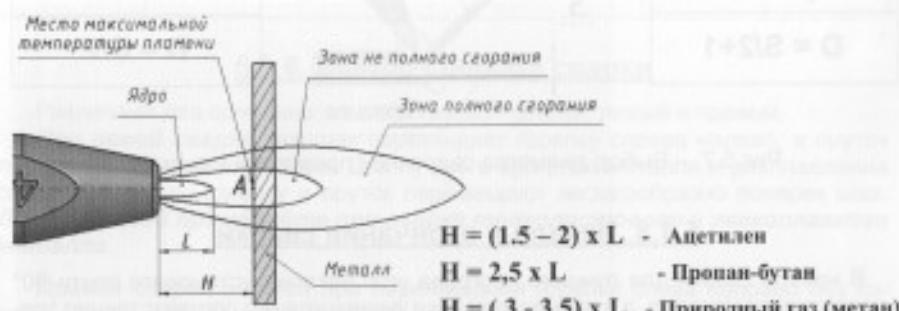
Расположение ядра пламени относительно свариваемого металла.
